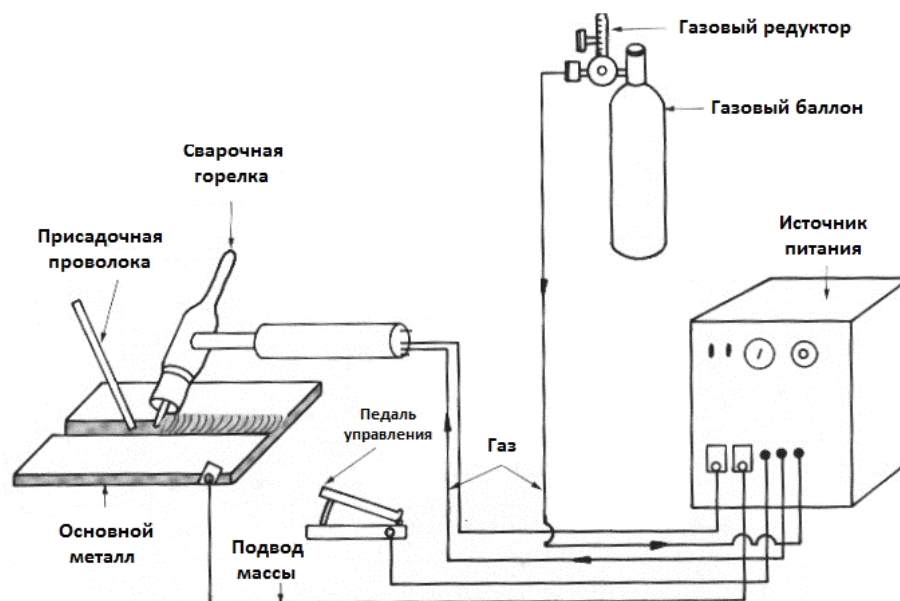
Схема установки для аргодуговой TIG сварки
